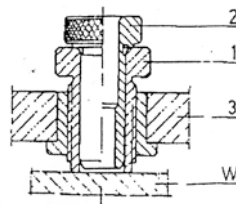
Sarung Pengarah Lepas Pasang Tipe E
